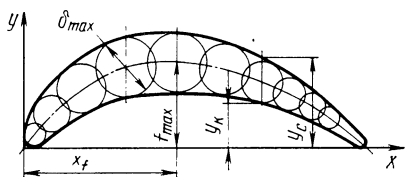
Лопаточный профиль с обозначением основных размеров
